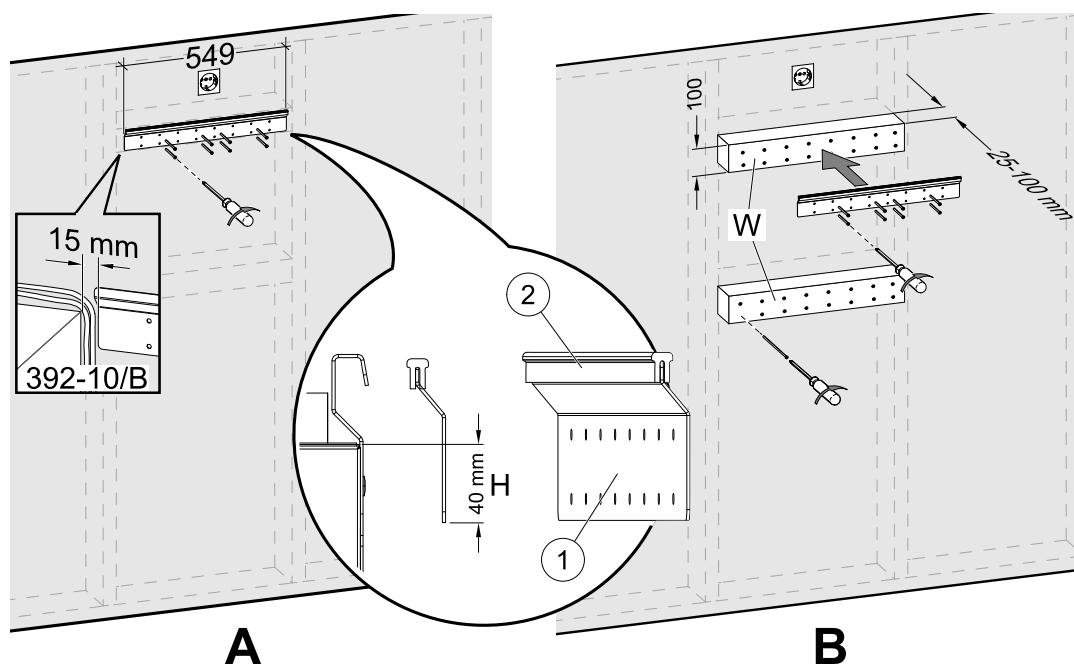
Installasjon av monteringsbrakett med eller uten utforing.
